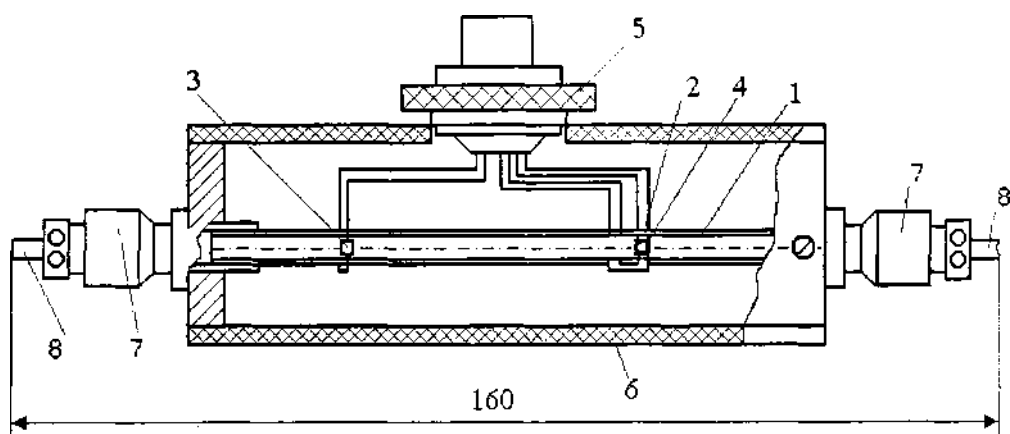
Конструкция трубчатого преобразователя расхода жидкости и газа на основе ТПТТ: 1 – трубка преобразователя; 2,3 – основной и компенсационный полупроводниковые термометры сопротивления; 4 –нагревательный элемент; 5 – штепсельный разъём; 6 – корпус преобразователя; 7 – ниппельные соединения типа конус-конус; 8 – внешний трубопровод.
